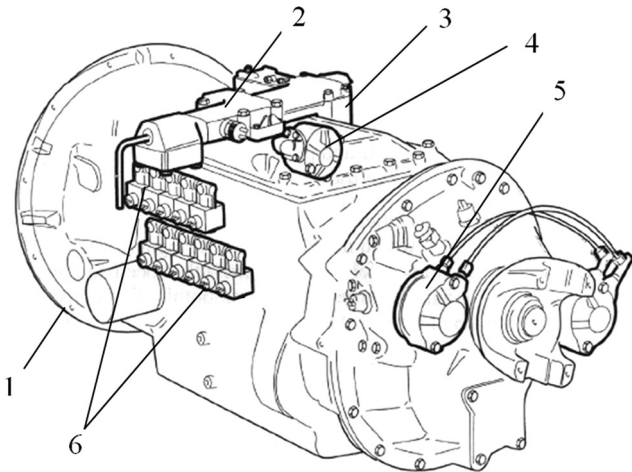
Автоматизированная 14-ступенчатая коробка передач GRS900 Scania: 1 — картер фрикционного сцепления, 2 — исполнительный механизм коробки передач, 3 — пневмоцилиндр поперечного хода, 4 — пневмоцилиндр продольного хода, 5 — пневмоцилиндр демультипликатора, 6 — рампа с ЭМК управления коробкой передач и механизмом отбора мощности
